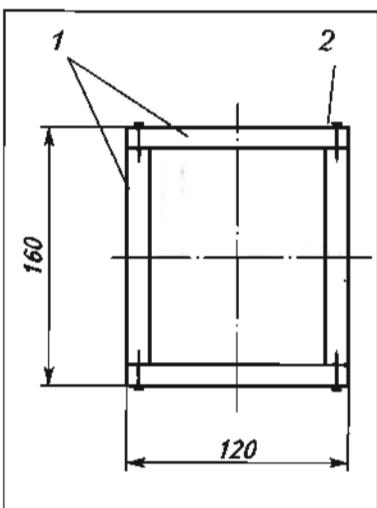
Схема крепления стенок домика: 1 — стенки, 2 — гвоздь
